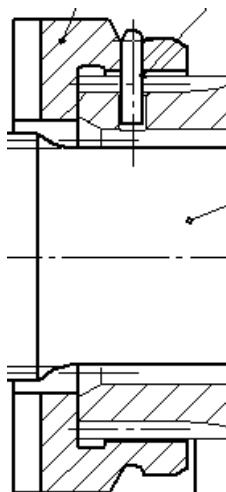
Общий вид шлицевого соединения полумуфты блокировки межколесного дифференциала и корпуса дифференциала
